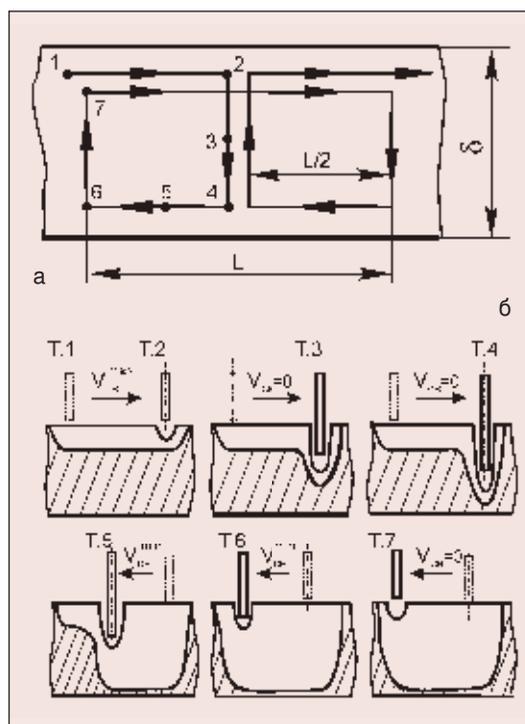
Схема перемещения торца электрода (дуги) в вертикальной плоскости стыка (а) и проплавления основного металла (б) при сварке по схеме I
